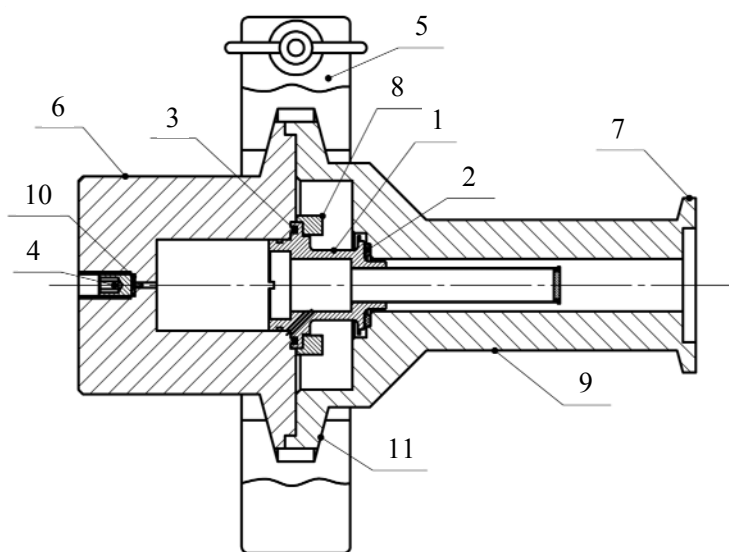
Конструкция приспособления для проверки герметичности: 1 – проверяемая гильза-держателя; 2, 3 – уплотнительные кольца; 4 – клапан; 5 – хомут; 6 – корпус; 7 – присоединительный фланец КФ; 8 – фланец; 9 – втулка; 10 – заправочное отверстие; 11 – фланец КФ
